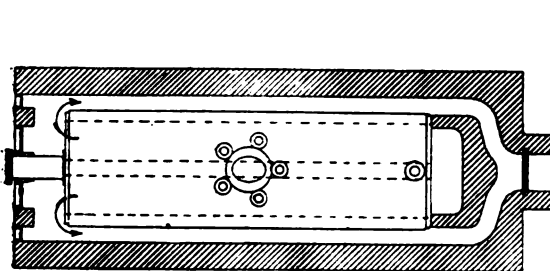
Grundriss zu Fig. 151. a Wasserstands-
